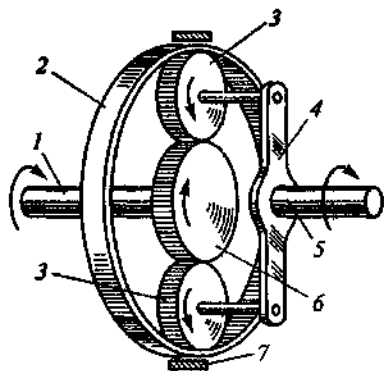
Планетарный механизм: 1 — ведущий вал, 2 — эпициклическая шестерня, 3 — сателлит, 4 — водило; 5 — ведомый вал, 6 — солнечная шестерня; 7 — тормоз
